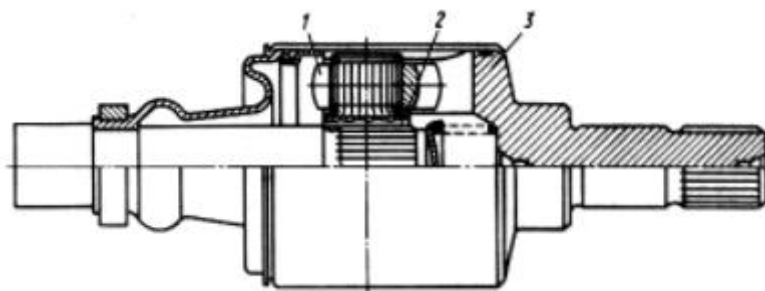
Трехшиповой универсальный карданный шарнир типа “Трипод”: 1 – ролики; 2 – ступица; 3 – цилиндрический корпус
